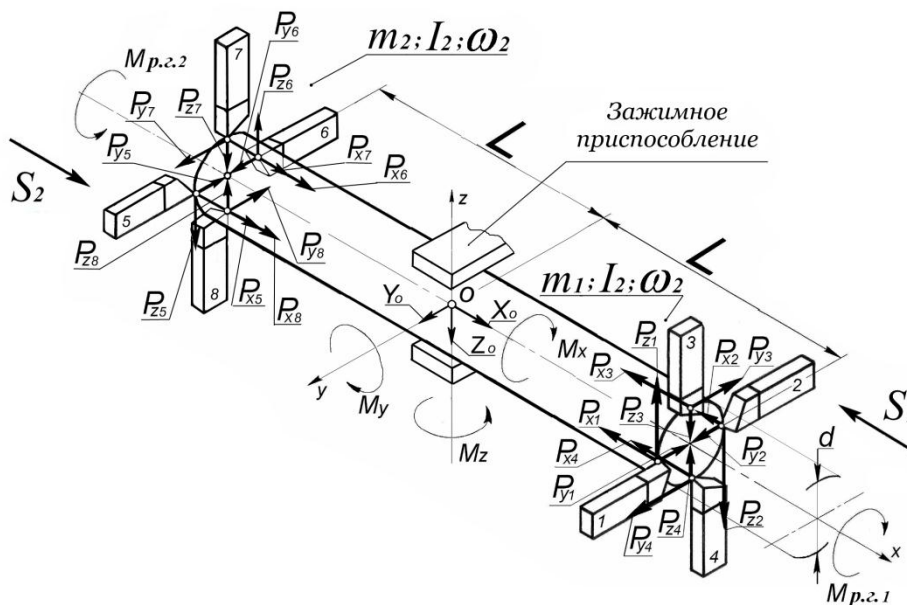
Расчетная схема нарезания резьбы на неподвижной заготовке из ПКМ резьбовыми головками с восемью режущими элементами
